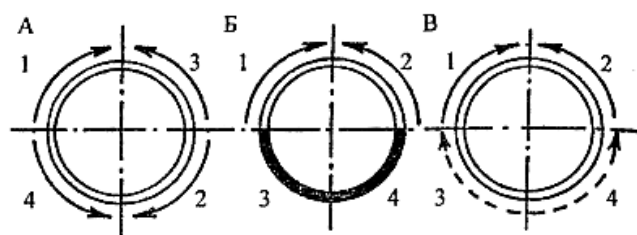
Сварка труб большого диаметра: А-до 300 мм; Б-до 600 мм; В-сварка без поворота трубы
